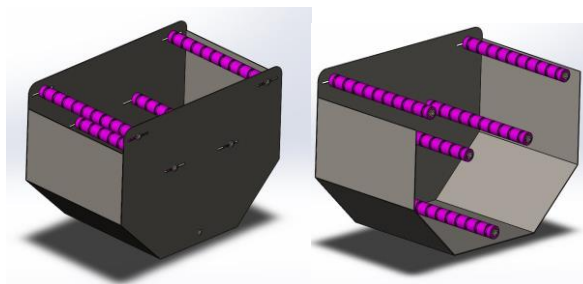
Diseño Paramétrico Impregnador de Resina
